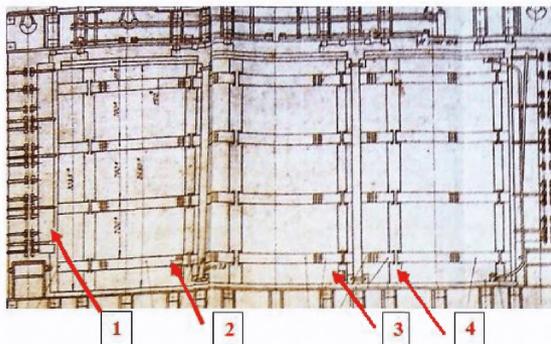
Эскиз конструкции с облегчающими обмотки ВН барьерами, барьерами на боковых ярах и зоны отбора образцов
